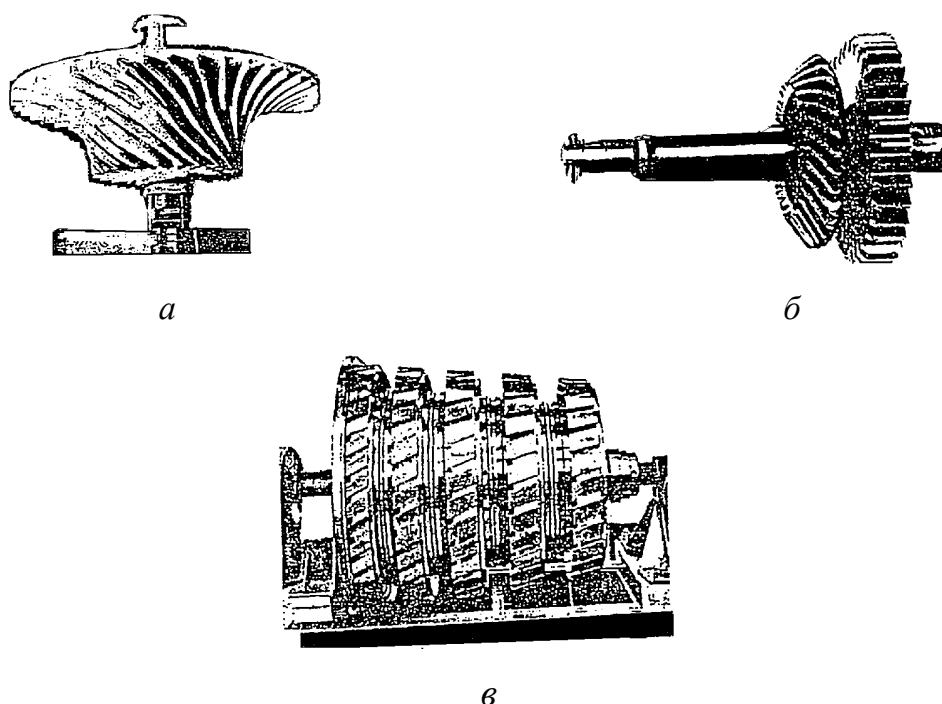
Корпус ротора газовой турбины из сплава ВЖЛ-14Н (*а*), шестерня из стали 18Х2НМА для судовых энергетических агрегатов (*б*), корпус компрессора из сплава ВТ8, полученные электронно-лучевой сваркой
